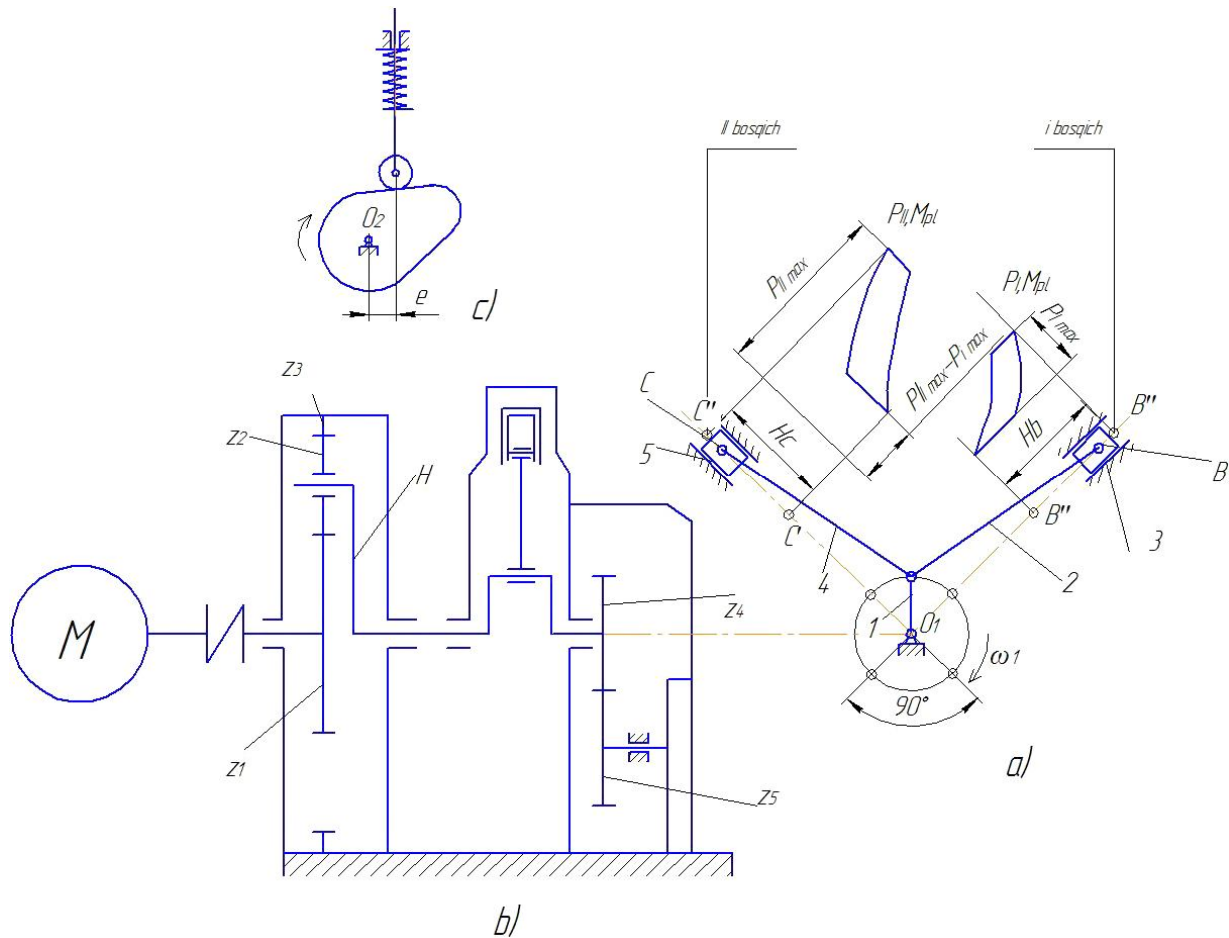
Кинематическая схема двухступенчатого воздушного компрессора
